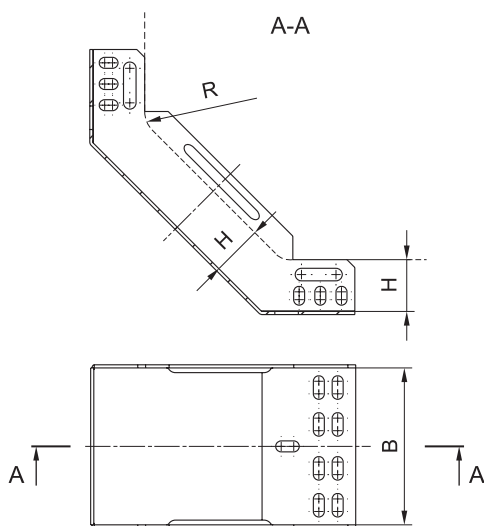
Поворот 90° вертикальный внутрь. Размеры для размещения кабеля /
